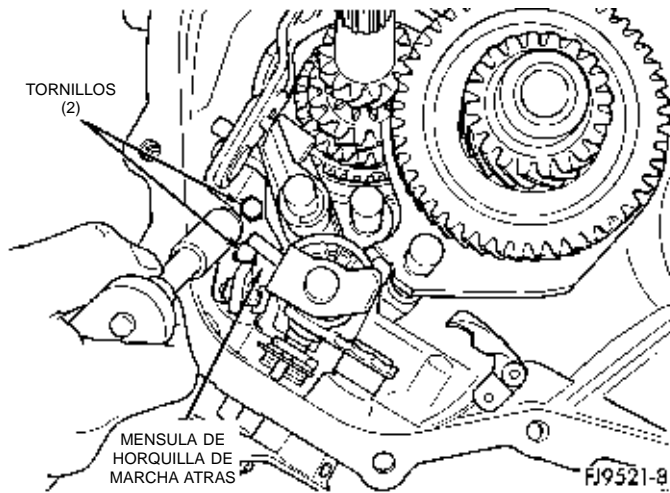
Desmontaje del engranaje secundario de marcha atrás
